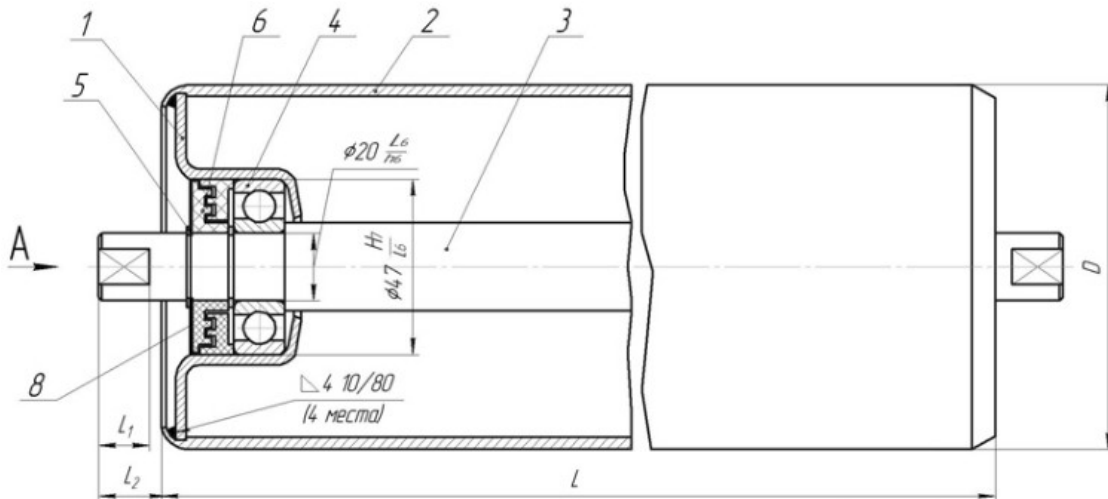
Ролик з підшипником кочення: 1 – обойма; 2 – корпус; 3 – вісь ролика; 4 – підшипники кочення; 5 – стопорне кільце; 6-8 – ущільнювальні кільця.
